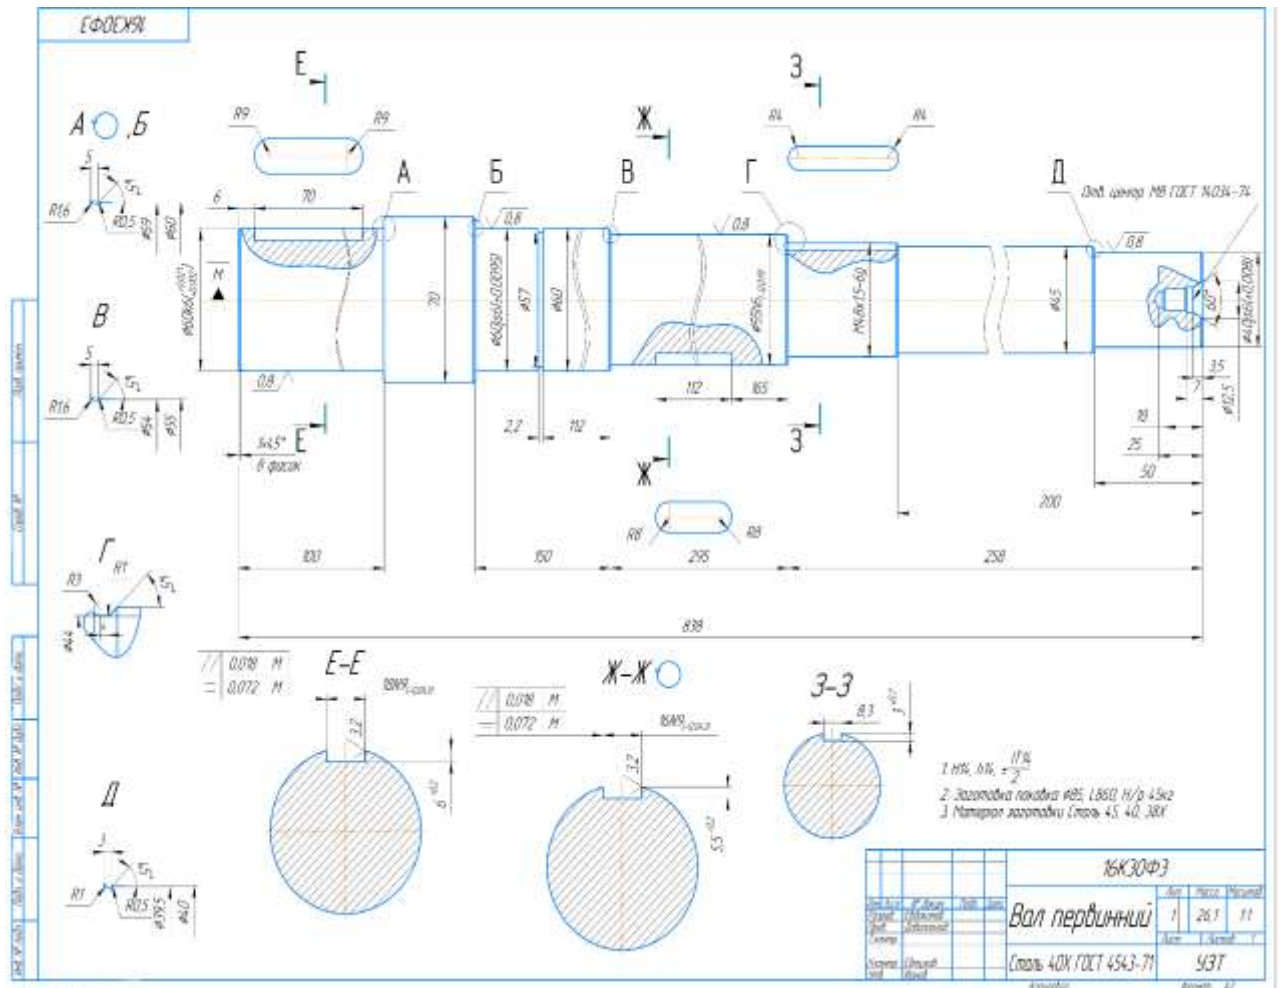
Робоче креслення деталі «Вал первинний».
